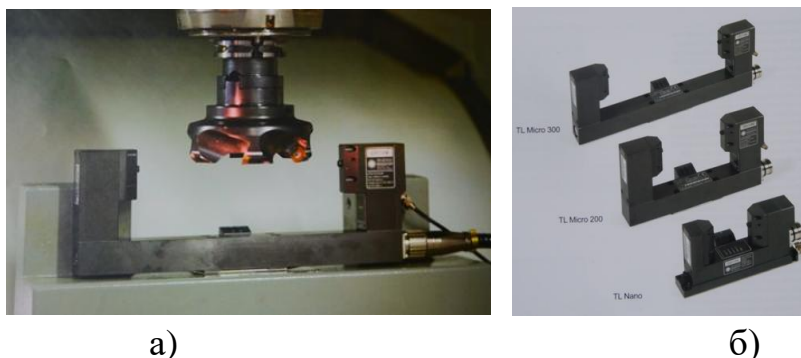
Лазерні системи вимірювання інструментів TL: а – на верстаті під час вимірювання; б – конструкції для різних розмірів інструменту
